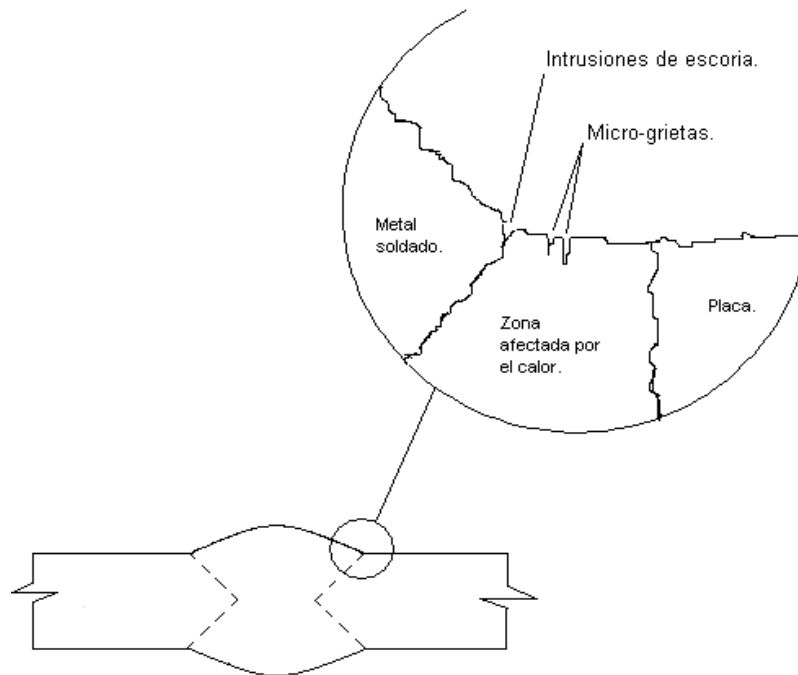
Incluso en soldaduras de sonido, los defectos están presentes, actuando como el sito o núcleo de la grieta. El factor de mella en fatiga de una soldadura es por lo tanto mucho más grande de lo que puede ser pronosticado de la geometría externa. Ref. [22]
